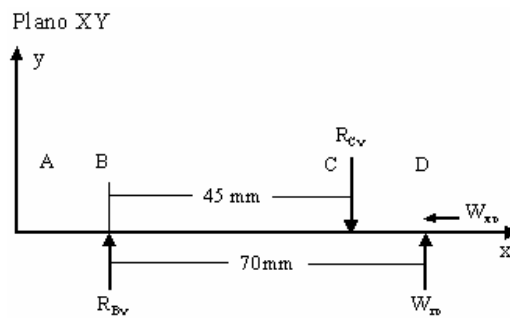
Cargas aplicadas en los apoyos del eje de la propela (plano XY)
